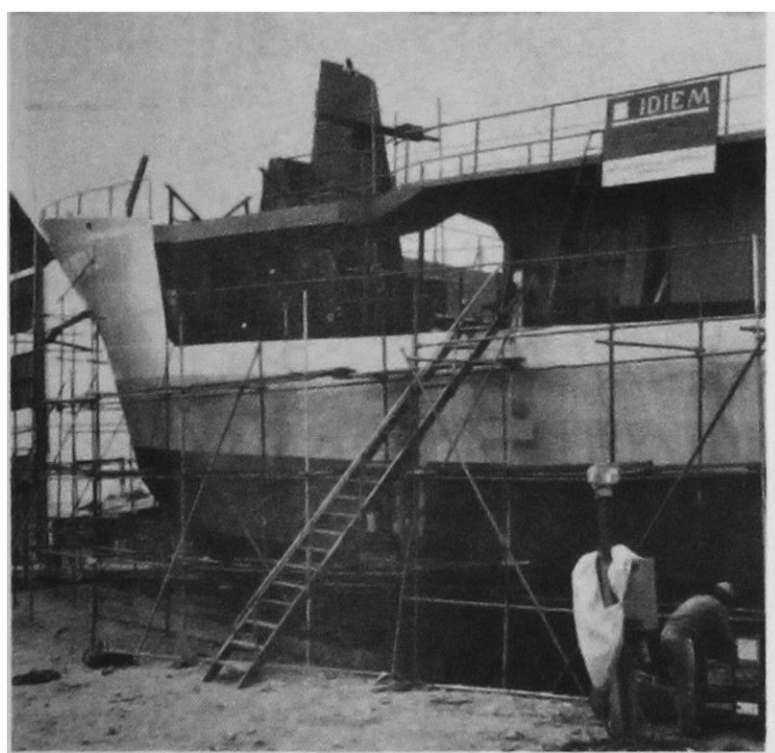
Control por rayos X de las uniones soldadas de un barco.
